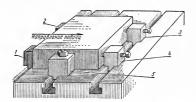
Крепление заготовки на столе поперечно-строгального станка;
